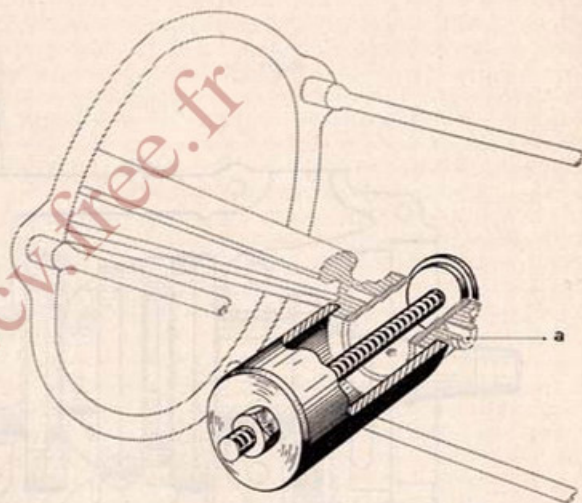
EXTRACTEUR MR-3682-10 POUR AXE DE PISTON
